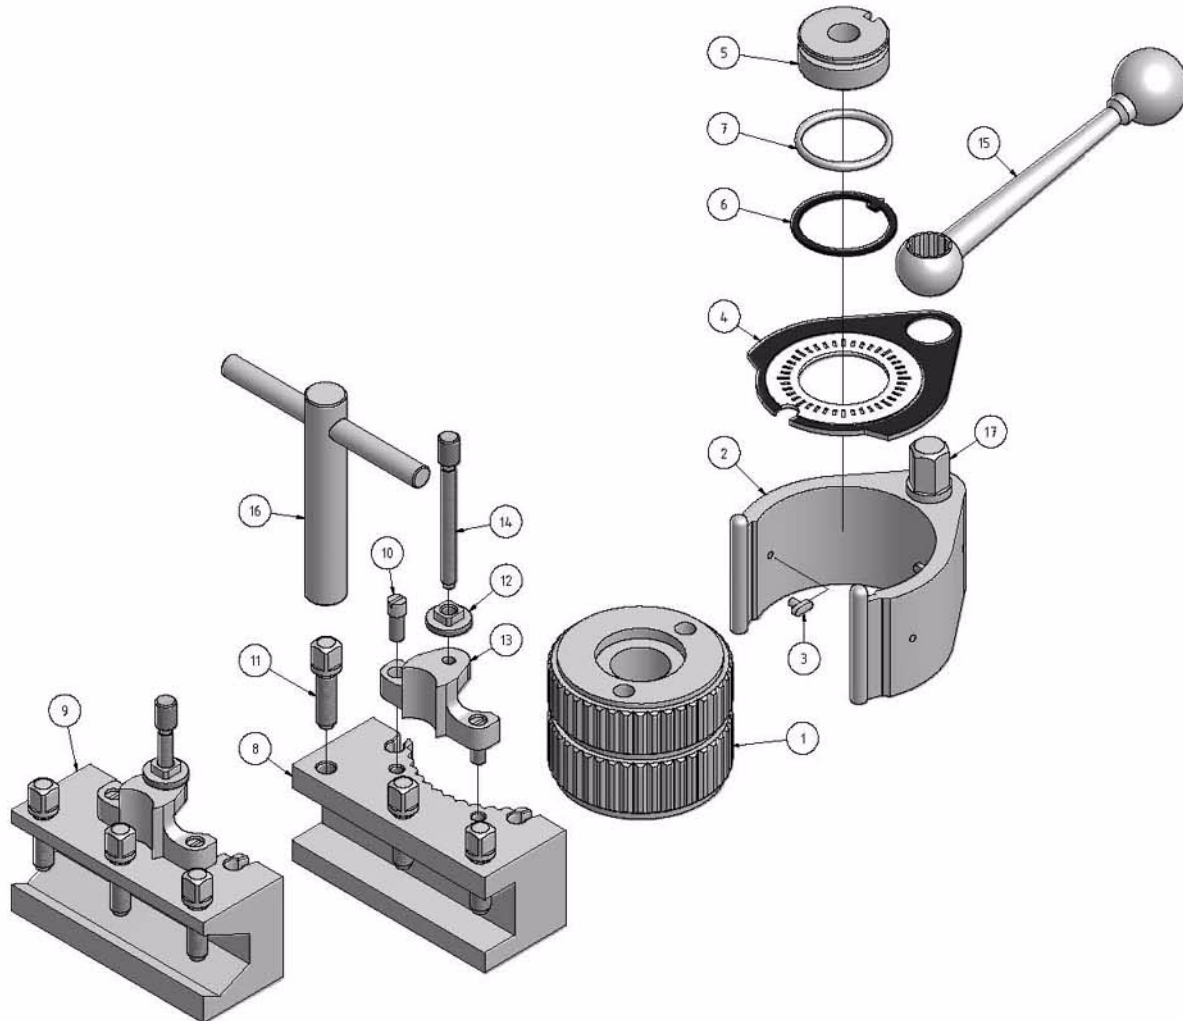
Ersatzteilzeichnung SWH 1-A/ 3-E - Drawing spare parts SWH 1-A/ 3-E
